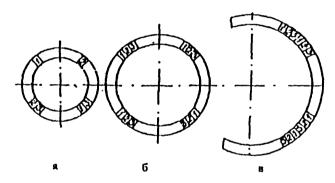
Схема отбора образцов для меланических испытачий сварных соединений труб диаметром: а) до 400 мм; б) от 400 мм до 1000 мм; в) 1000 мм и более: 1 - образец для испытаний на растяжение; 2 - образец для изгиба корнем шав наружу или на ребро; 3 - образец для изгиба корнем шав внутрь или на ребро.
